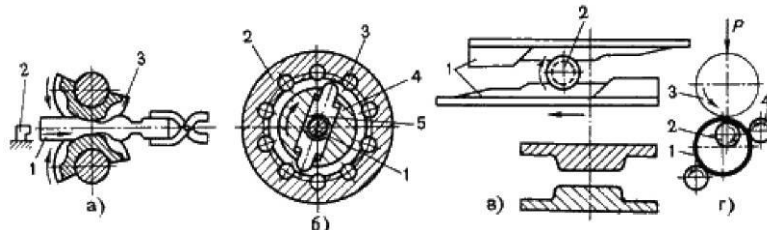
Схемы действия ковочных вальцов (а), ротационно-ковочной машины (б), станков поперечно-клиновой прокатки (в); раскатки (г)
